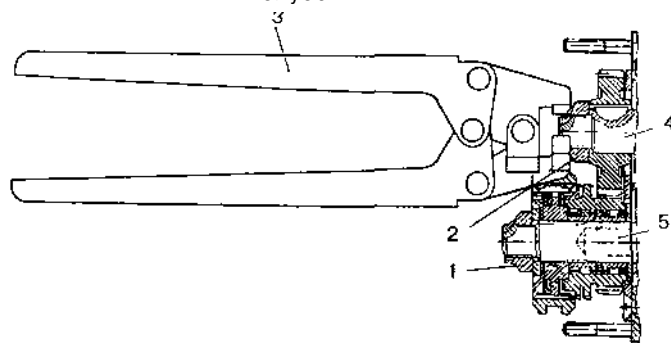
Стопореие гаек ведущего и ведомого валов коробки передач:
